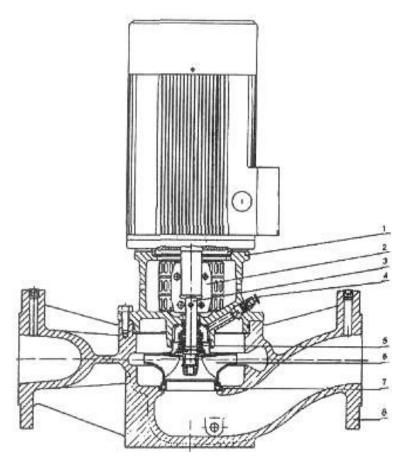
Конструкция насоса КЛМ: 1 — корпус насоса; 2 — подшипник; 3 — вал насоса-двигателя; 4 — подвод жидкости для гидравлического уплотнения; 5 — торцевое уплотнение вала; 6 — рабочее колесо; 7 — уплотнительное кольцо; 8 — присоединительный всасывающий патрубок
